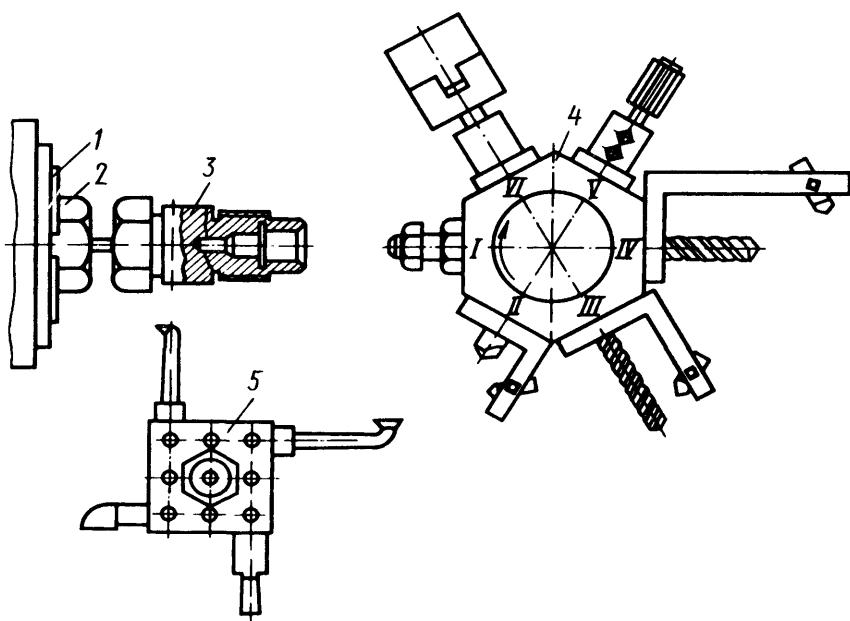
Пример обработки на токарно-револьверном станке с револьверной вертикальной головкой:
